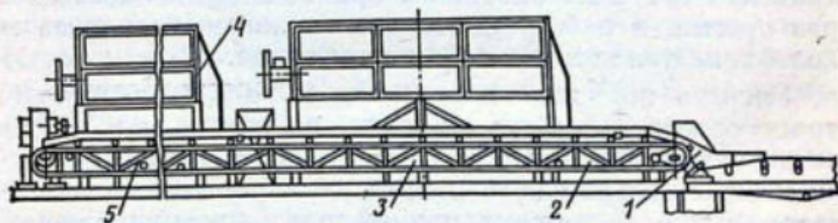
Ленточный транспортер КПГ-10.46.16 в сборе:
